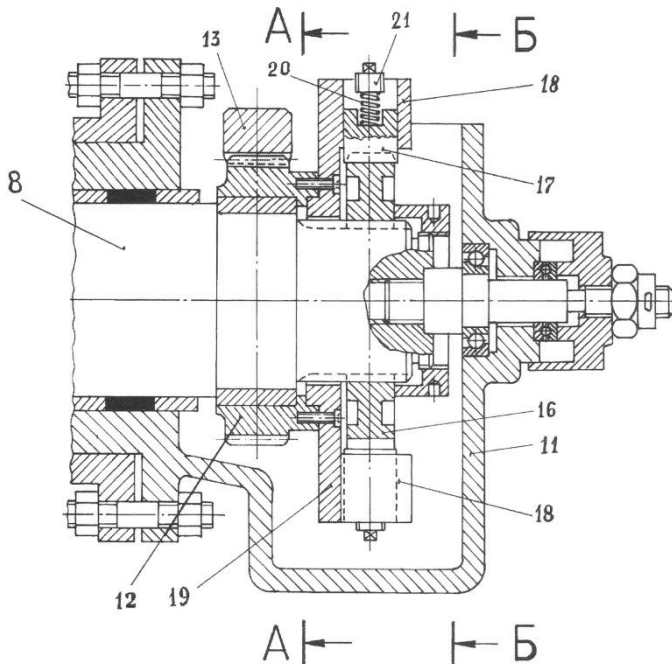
Хвостова частина дрилі (місце I на рис. 2) з елементами механізму кантування: 8 – дріль; 11 – кронштейн; 12 – зубчасте колесо; 13 – зубчата рейка; 16 – храпове колесо; 17 – собачка; 18 – кармани; 19 – планшайба; 20 – пружина; 21 – різьбова пробка.
